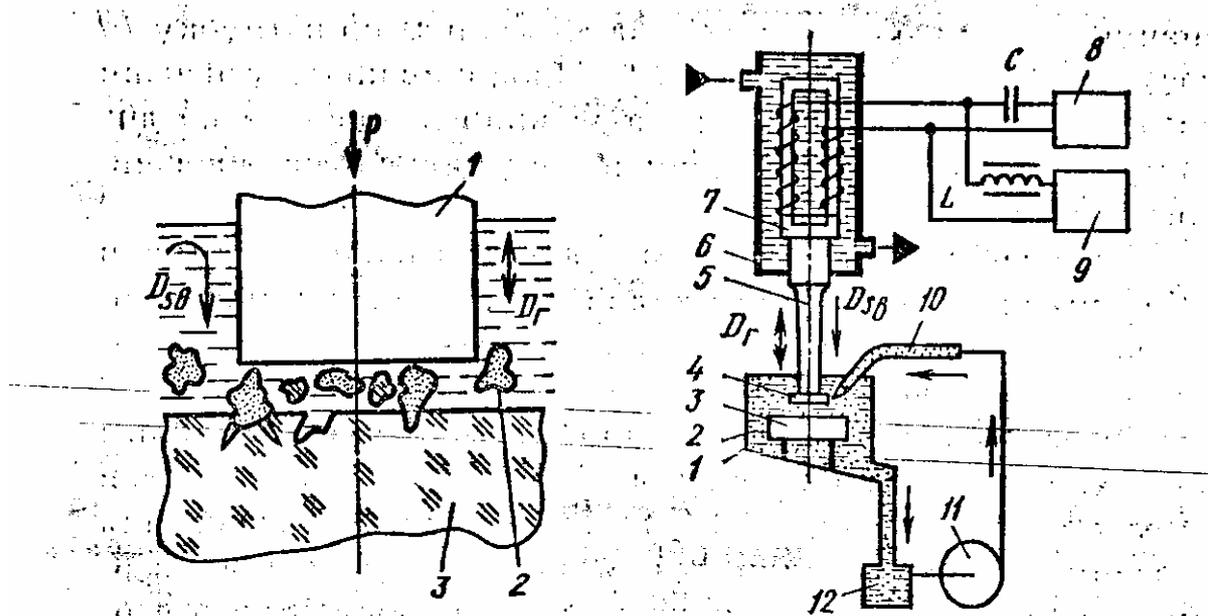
Схема разрушения обрабатываемого материала при УЗ-обработке и основные узлы УЗ-станка
